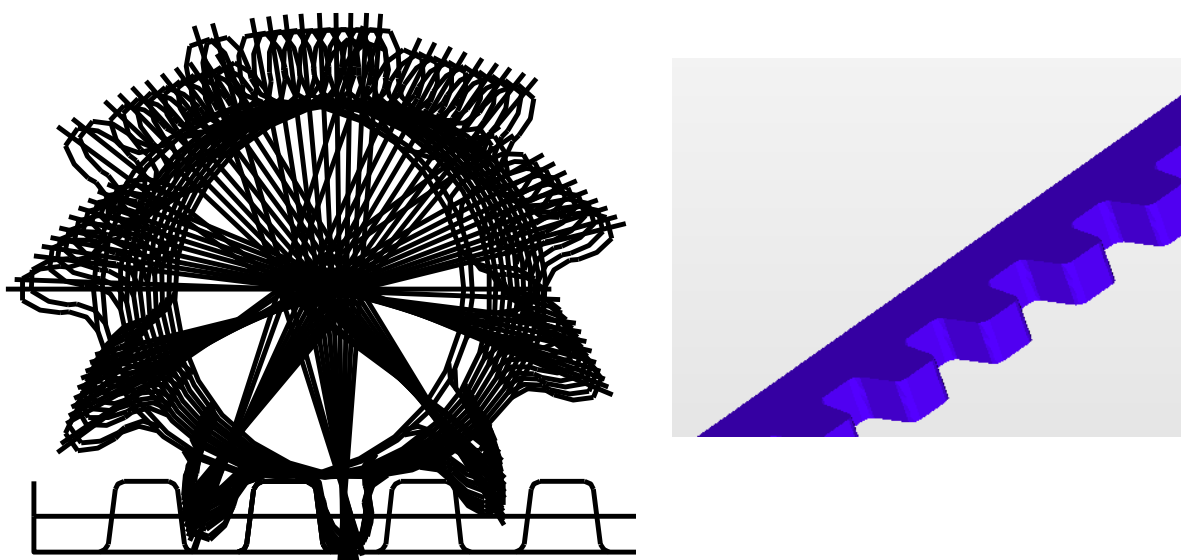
Кинограмма зацепления пары зубчатое колесо – зубчатая рейка (шаг зацепления $p=80$ мм) и общий вид рейки
